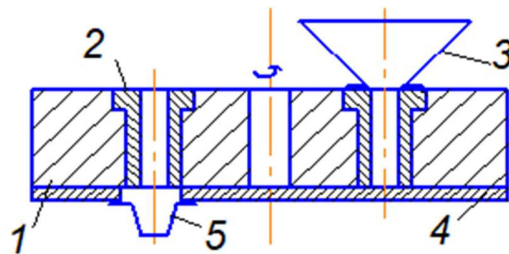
Дисковий дозатор: 1 – диск, що обертається; 2 – мірний стакан; 3 – бункер; 4 – нерухомий стіл; 5 – направляюча лійка
